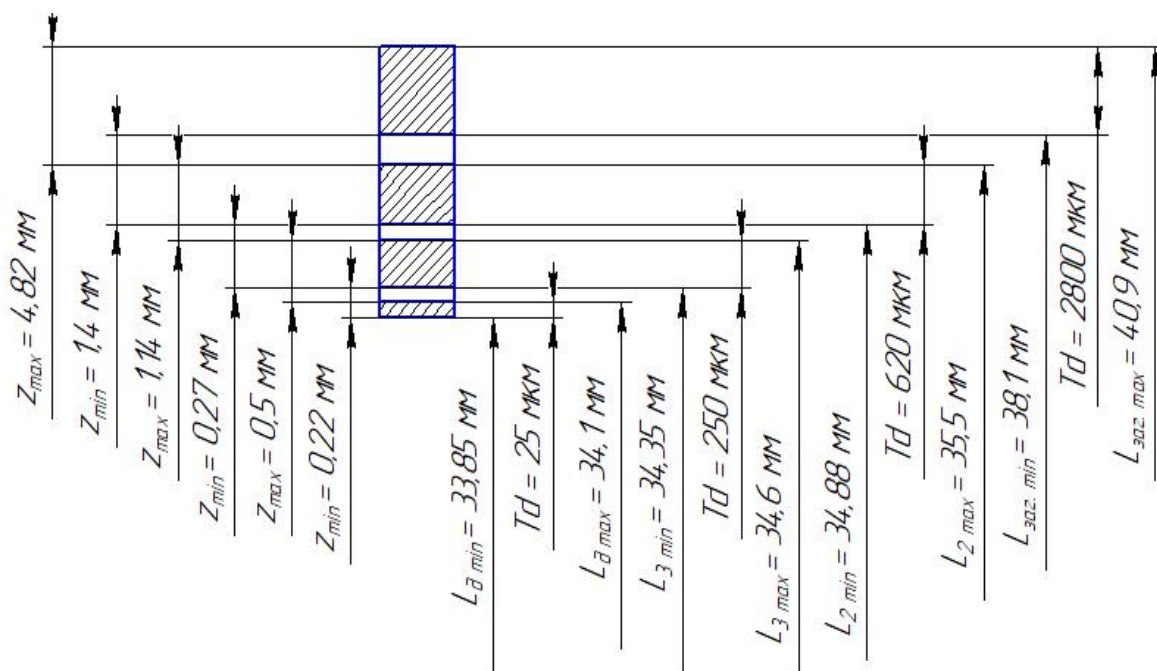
Схема графического расположения припусков допусков на обработку поверхности 34,1h7 (-0,025)
